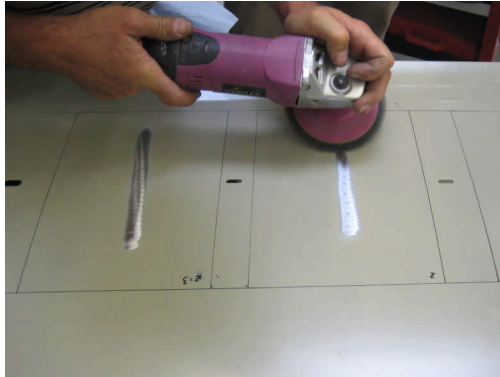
Entlacken vor dem Aufschweißen der Bits
